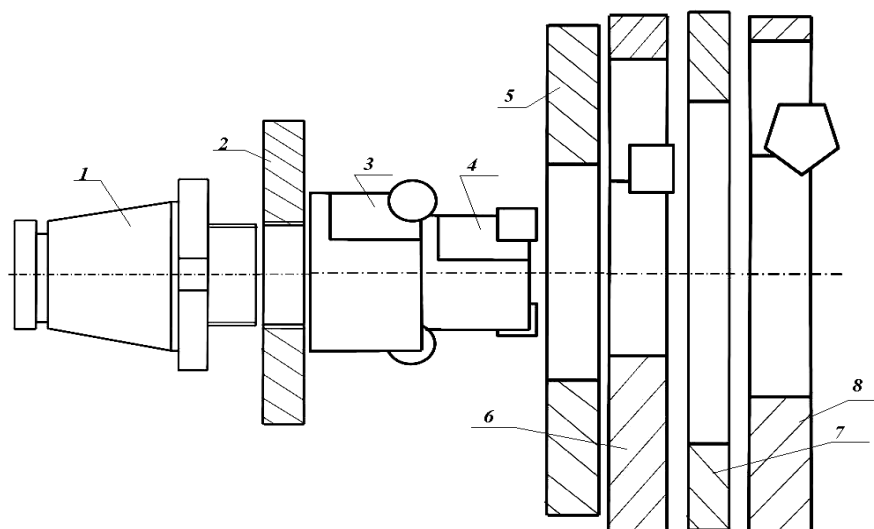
Схематичное изображение частей конструкции универсально-сборного комбинированного металлорежущего инструмента
